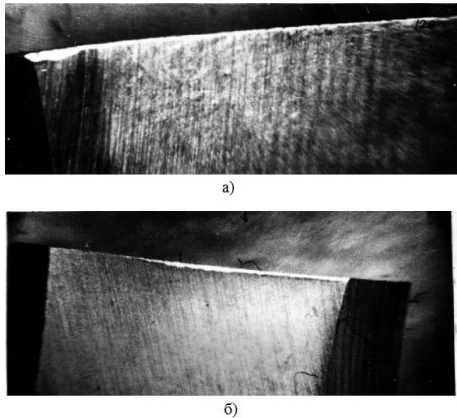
Типовий знос зубів фрези з роздільною схемою формоутворення по заднім граням після оброблення зубчастого вінця  $m = 20$  мм;  $z = 316$ ;  $b = 800$  мм: а - зуб правого корпусу; б - зуб лівого корпусу
